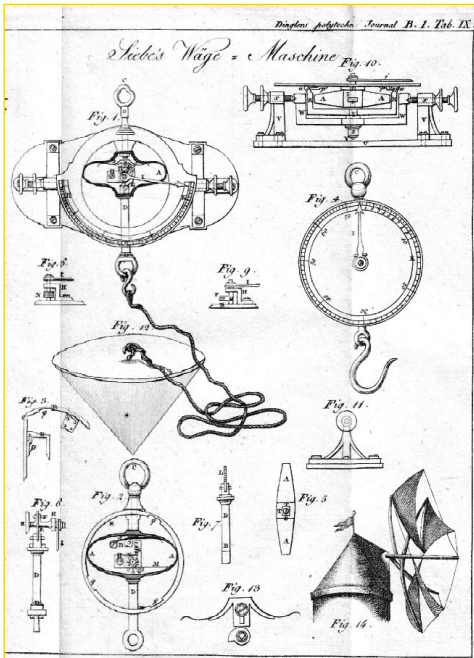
Polytechnisches Journal Bd. 1/1820 Siebe's Waage=Machine
